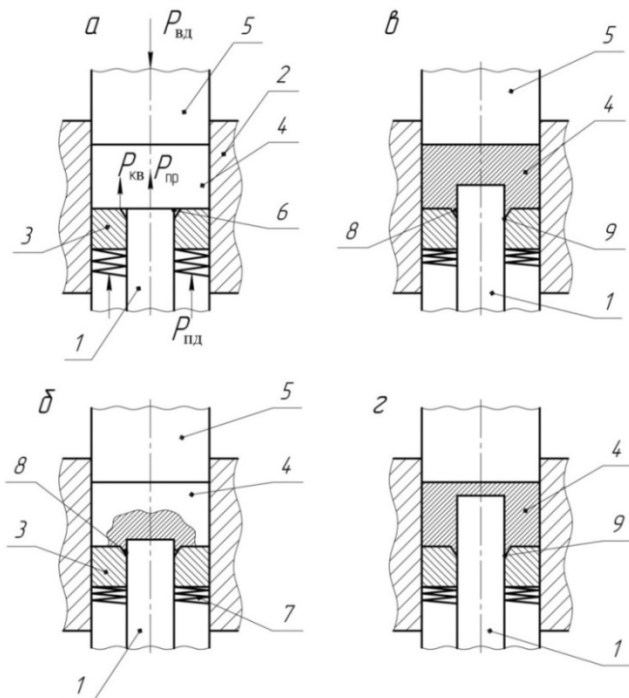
Сборка металлических заготовок пластическим деформированием с глубокой зачисткой контактных поверхностей:
